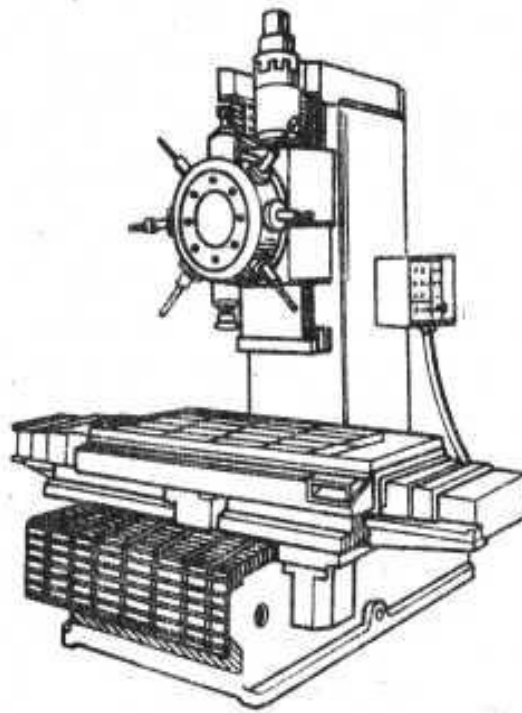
Схема устройства смены шпиндельного узла в виде револьверной головки
